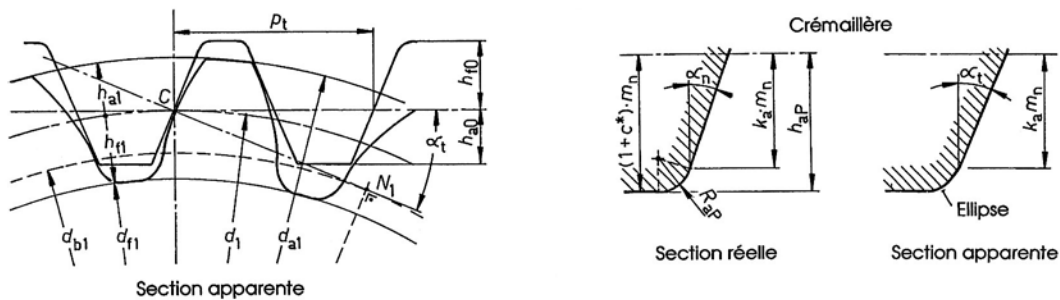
Dimensions générales d'un engrenage à crémaillère à denture hélicoïdale
